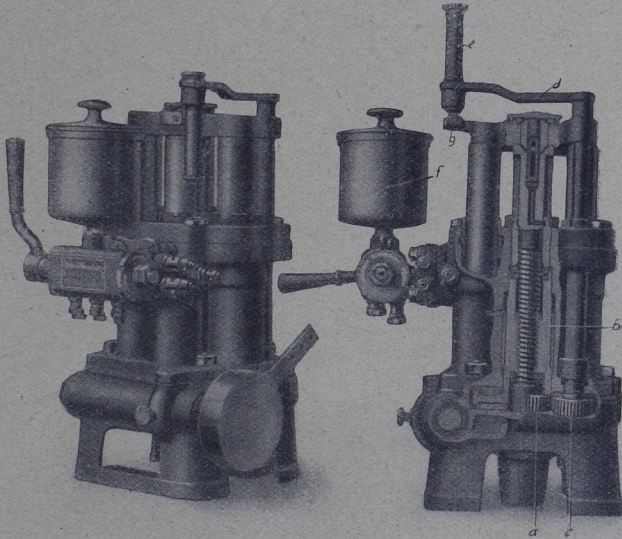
Schmierpresse „Dicker & Werneburg“.
